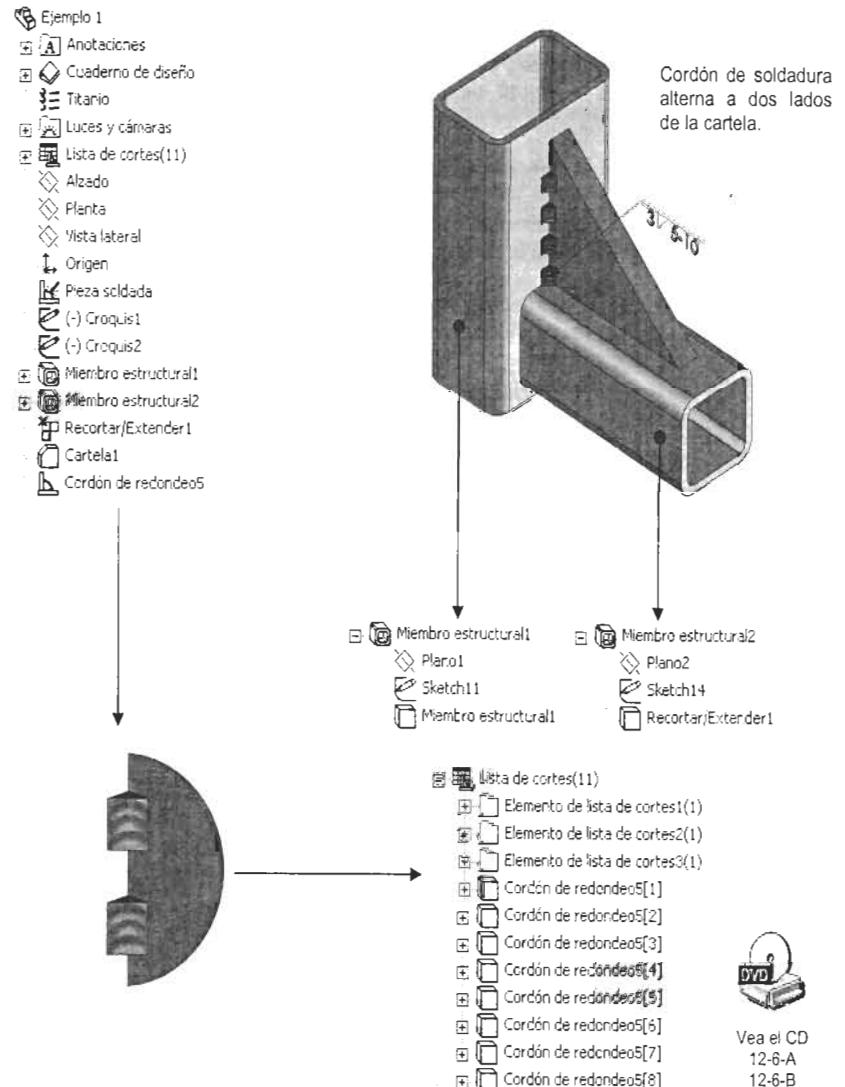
Gestor de Diseño en operaciones de Piezas Soldadas.
